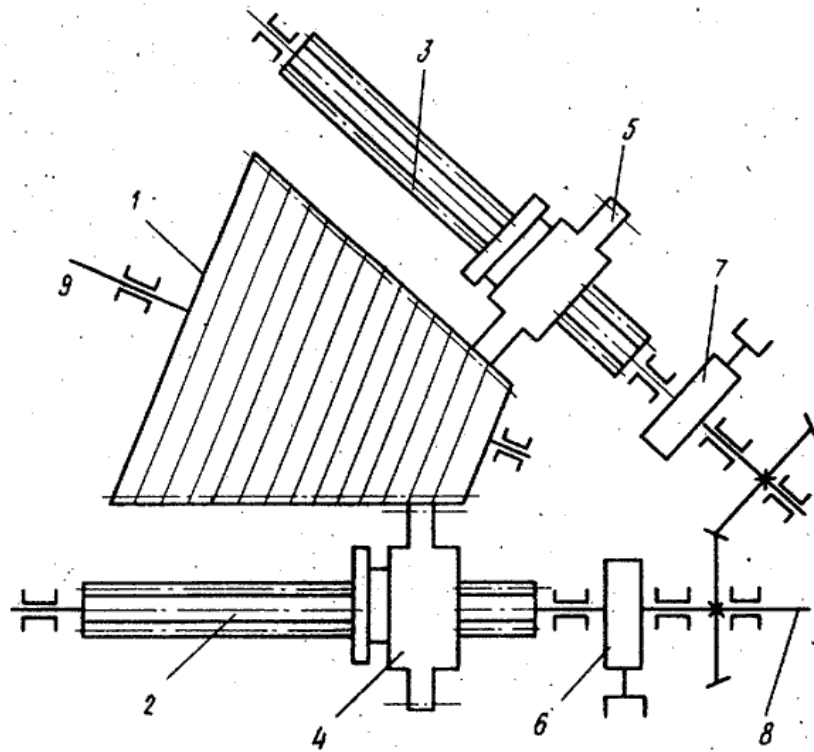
Зубчатий варіатор: 1 – блок евольвентно-конічних коліс; 2 – основний шліцевий вал; 3 – додатковий шліцевий вал; 4, 5 – зубчасті колеса; 6 – муфта; 7 – додаткова електромагнітна муфта; 8 – вал ведучий
